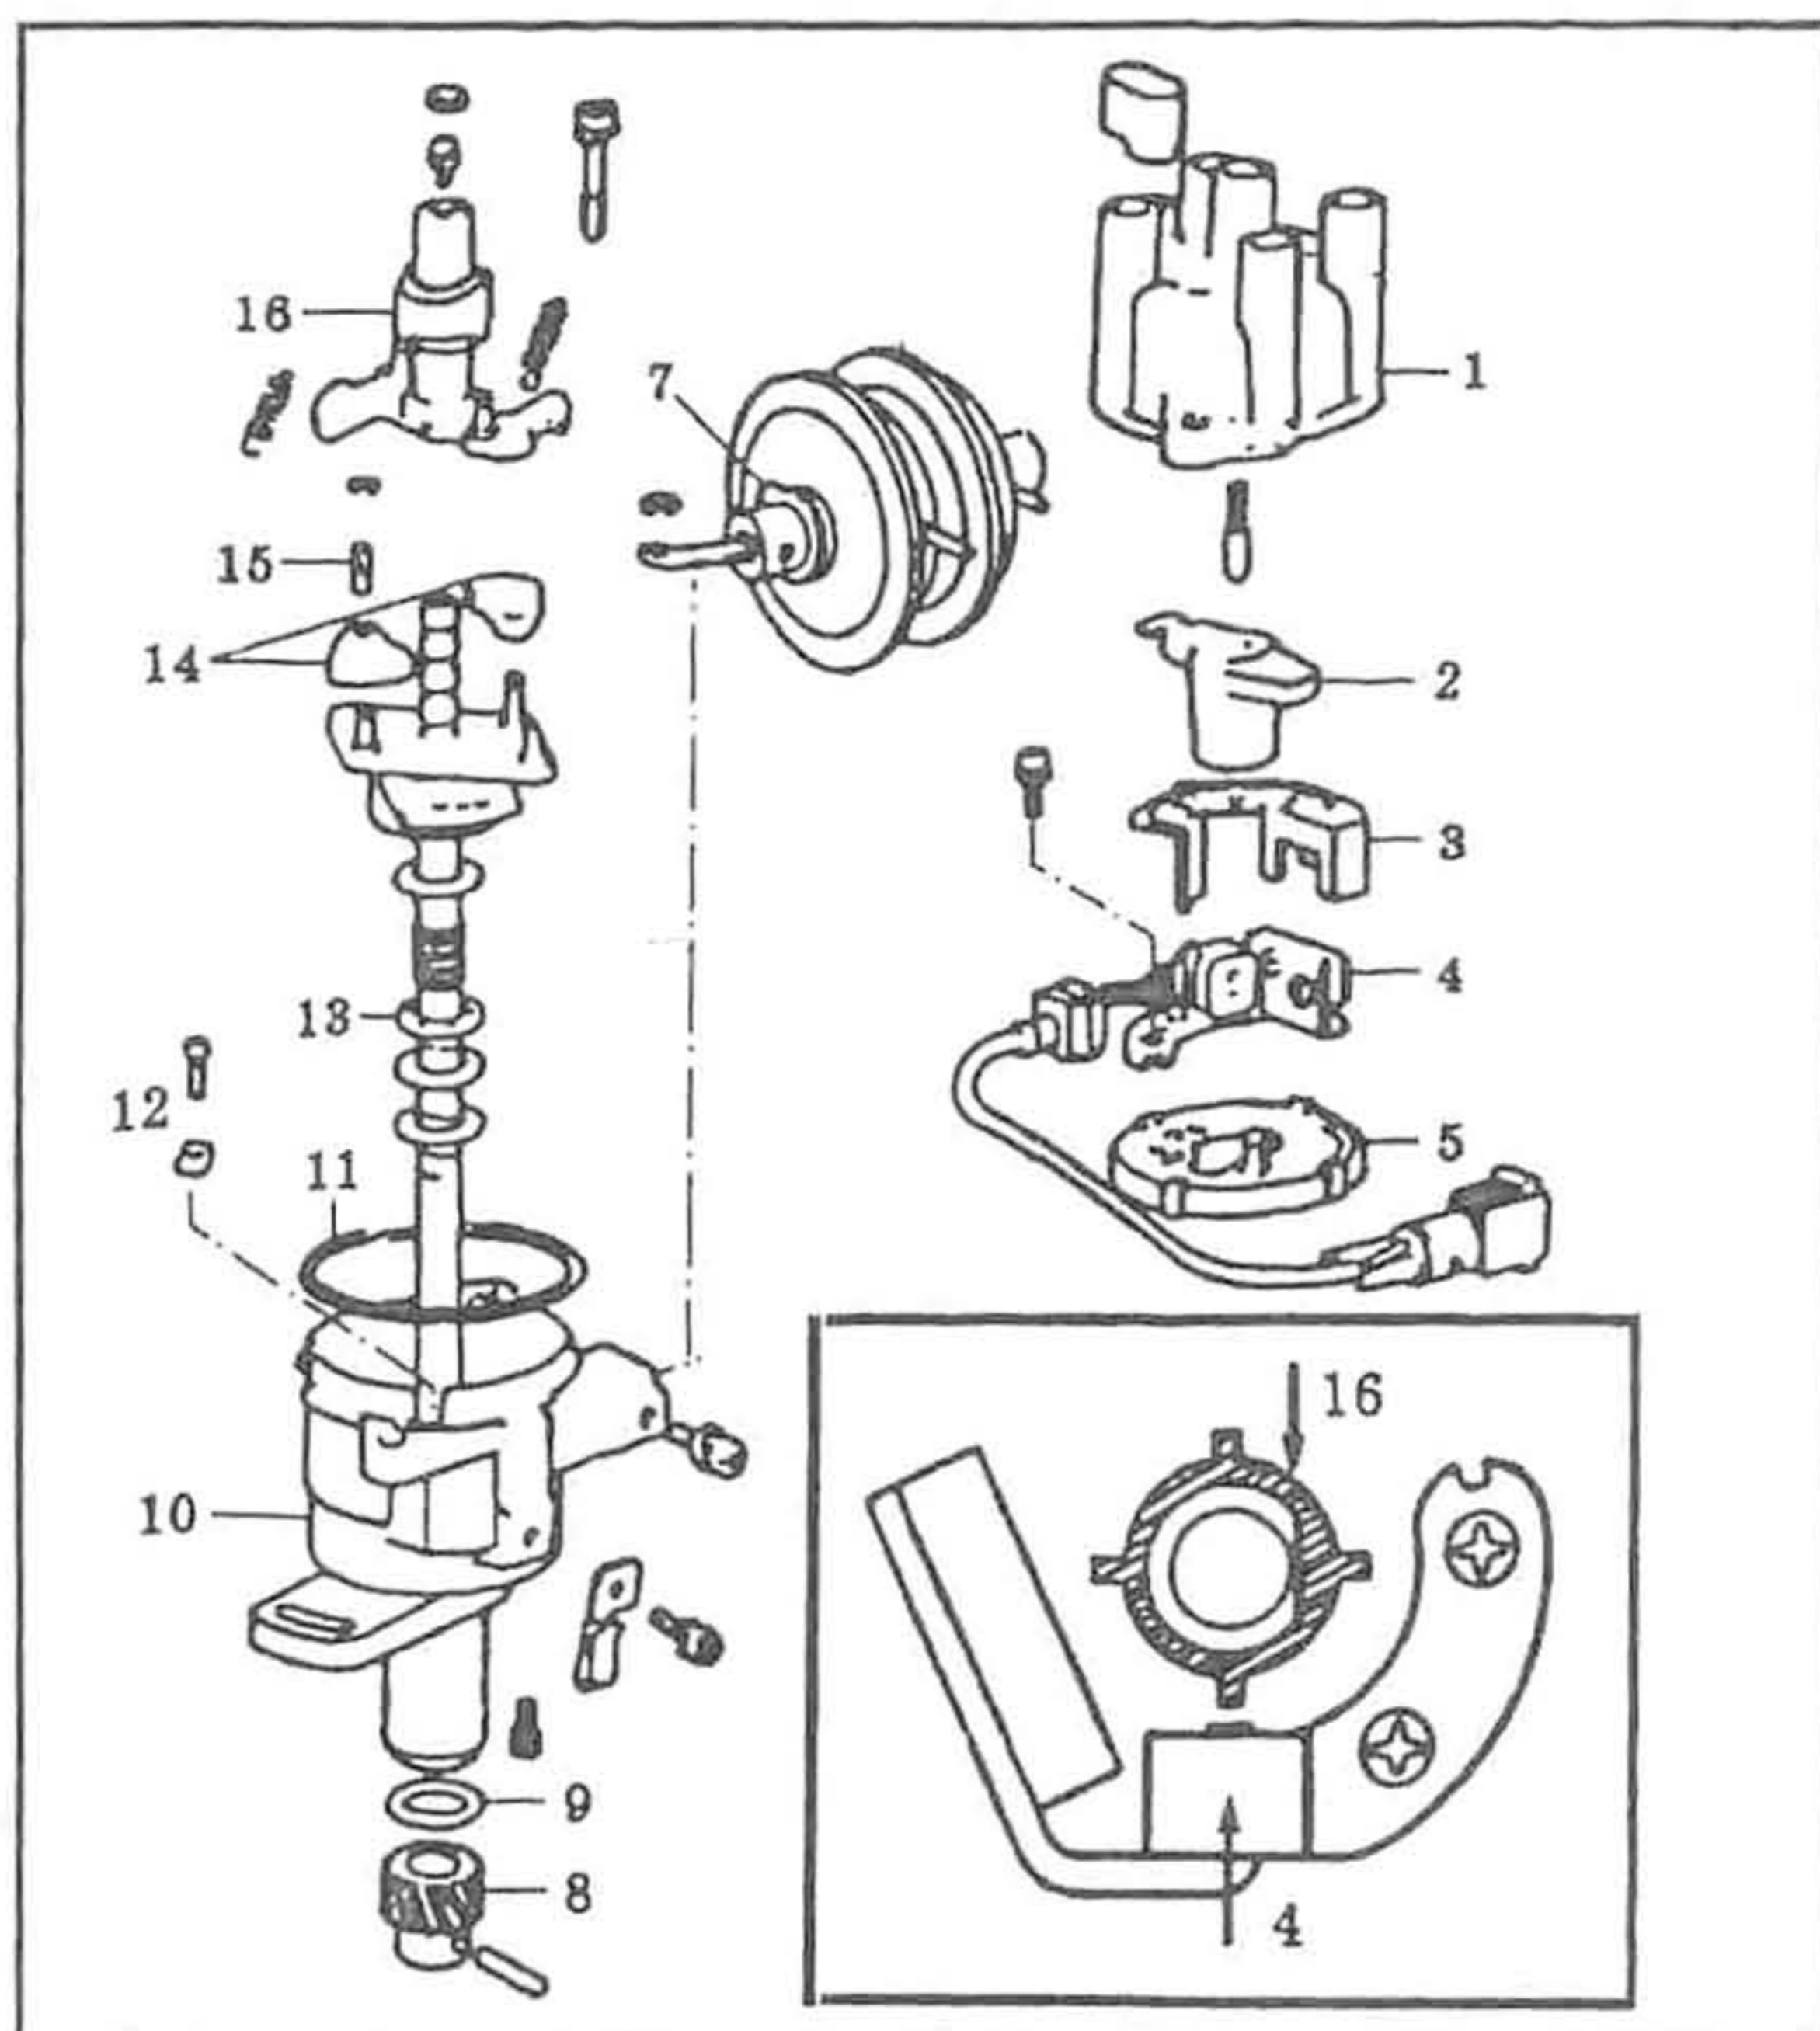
1. Крышка. 2. Бегунок. 3. Пылезащитный колпачок. 4. Сигнал-генератор. 5. Пластина прерывателя. 6. Диафрагма вакуумного устройства опережения зажигания. 7. Прокладка. 8. Шестерня привода распределителя. 9. Уплотнительное кольцо. 10. Корпус. 11. Уплотнительное кольцо. 12. Упорный подшипник. 13. Вал регулятора. 14. Грузики. 15. Подшипник. 16. Сигнал-ротор.
